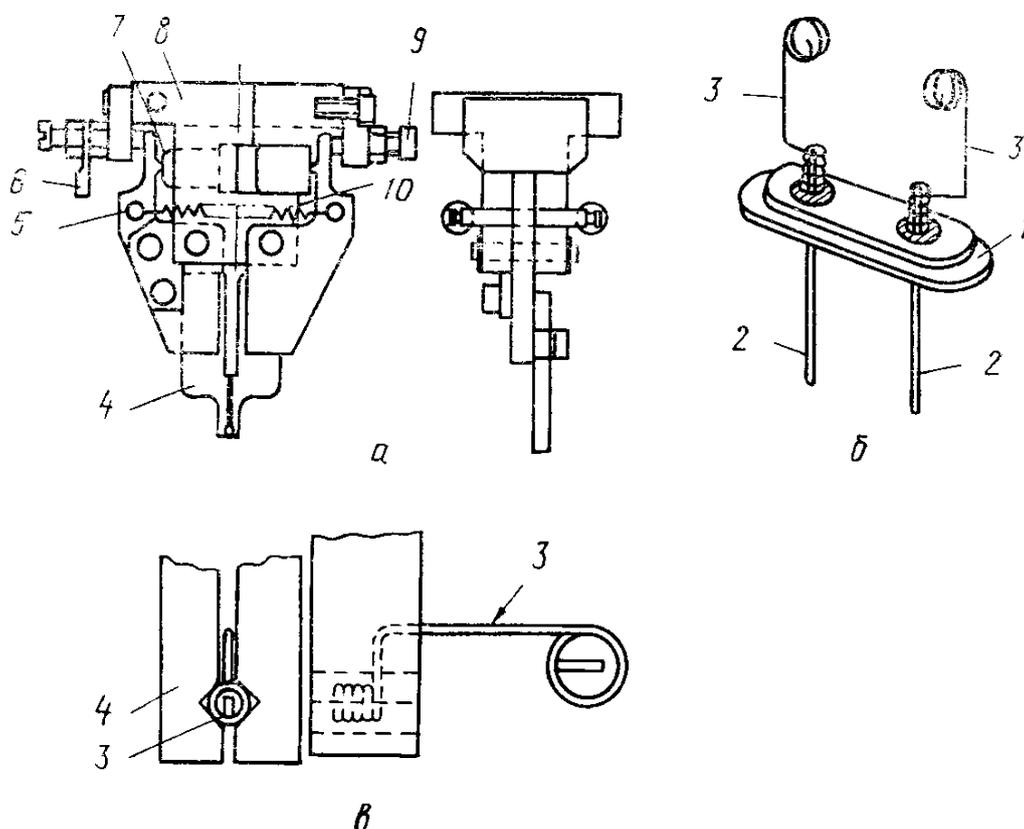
Захватное устройство (а) для установки фасонной пружины (б, в)
